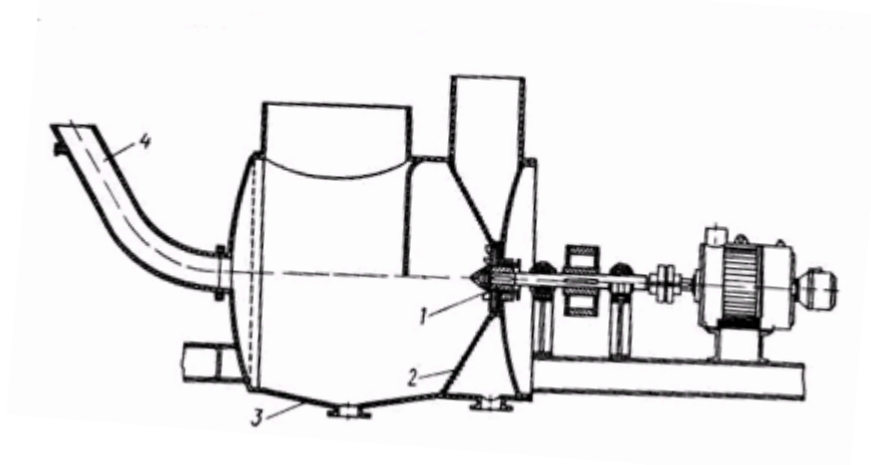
Схема гидроразбивателя горизонтального типа: 1- ротор; 2- сито; 3- ванна; 4 –патрубок отвода включений
